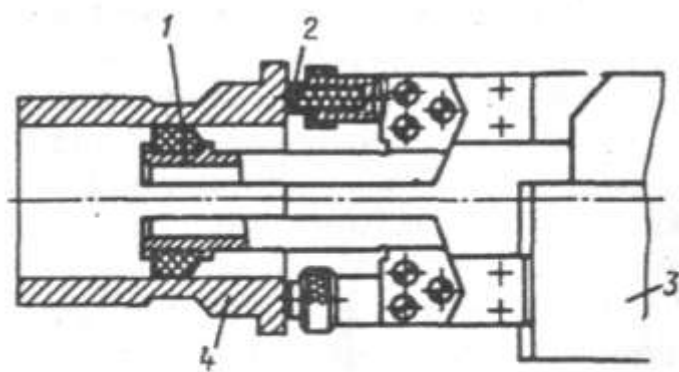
Хватное устройство с подпружиненными плунжерами.
